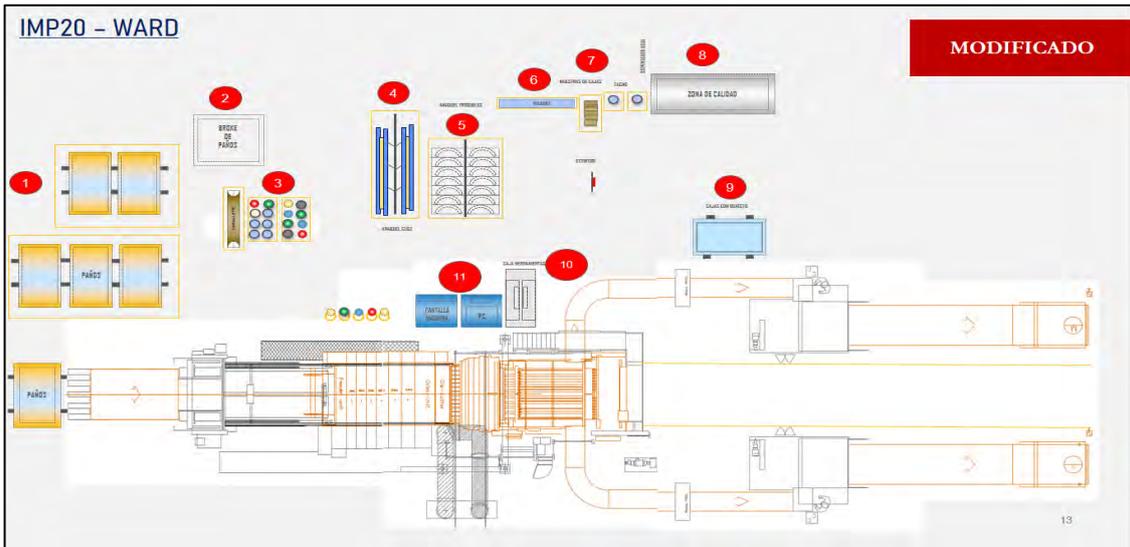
Layout zona de trabajo Imprenta 20 - Modificado
